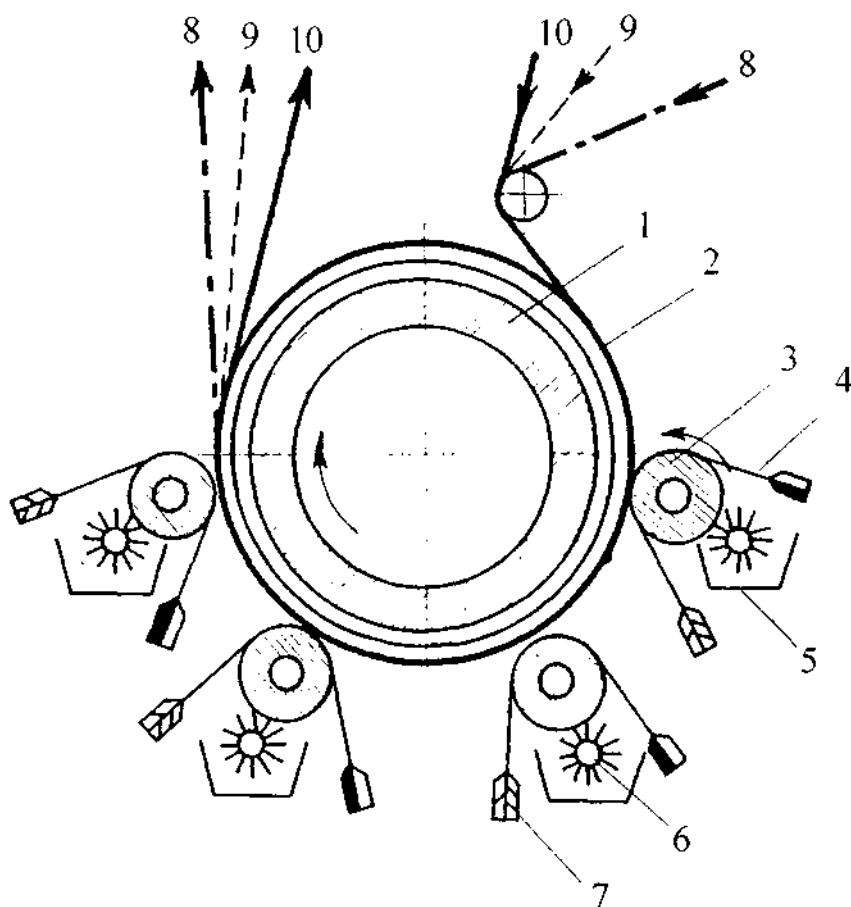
Принципиальная схема многовальной тканепечатной машины: 1 - грузовик; 2 - упругое покрытие (лапинг); 3 - печатные валы; 4 — ракля; 5 — корыто с краской; 6 — цилиндрическая щетка или обрезиненный валик; 7 — контрракля; 8 — печатаемая ткань; 9 — чехол; 10 — кирза
